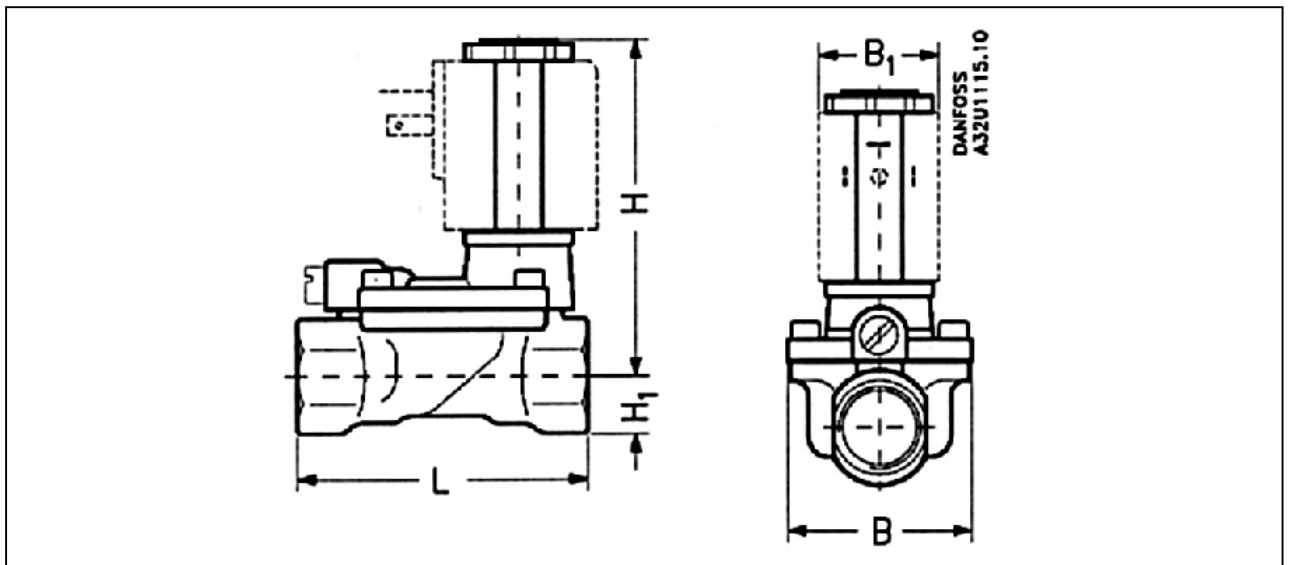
Габаритные и присоединительные размеры соленоидного клапана.
